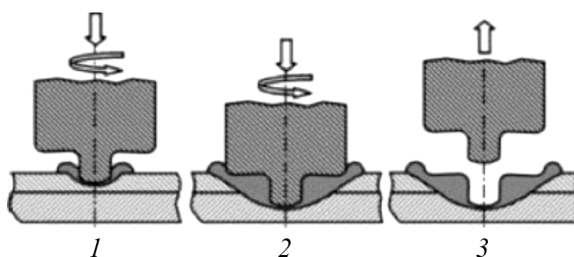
Схема ТСТП: 1 – погружение инструмента; 2 – перемешивание металла деталей (образование сварного соединения); 3 – вывод инструмента
